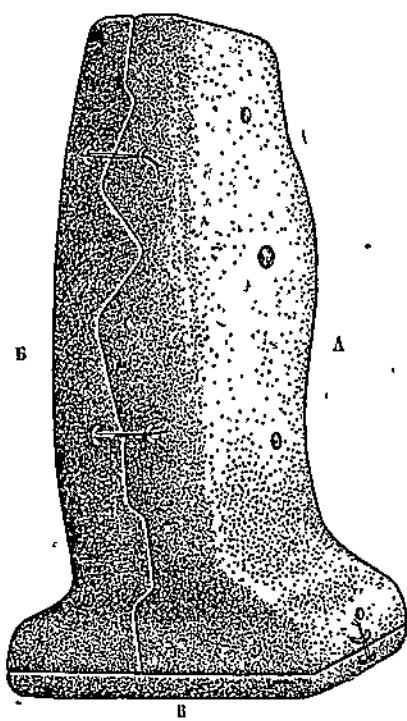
Изготовление kleевой формы на круглую скульптуру. Внешний вид готового кожуха. А, Б — передняя и задняя раковины, В — плитка. Все части кожуха соединены друг с другом тонкой проволокой, продетой через проволочные петельки, вделанные в части кожуха при наливке их.
